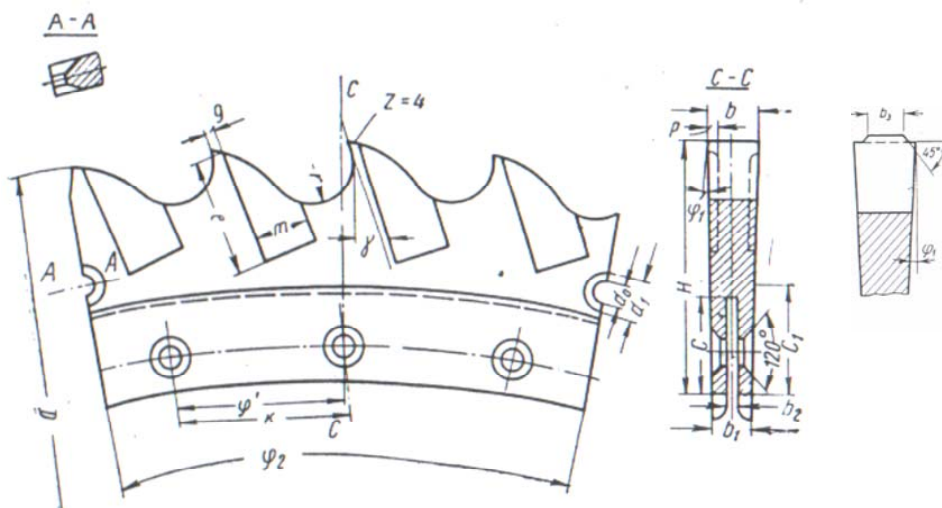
Зубчатые сегменты из быстрорежущих сталей для установки на дисковых пилах
